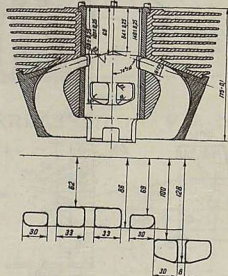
Цилиндр двигателя ИЖ-57 и его развертка (внизу).
